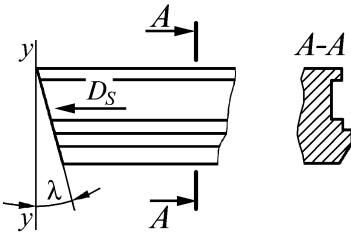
Тангенциальный фасонный резец, обеспечивающий плавное врезание в заготовку
